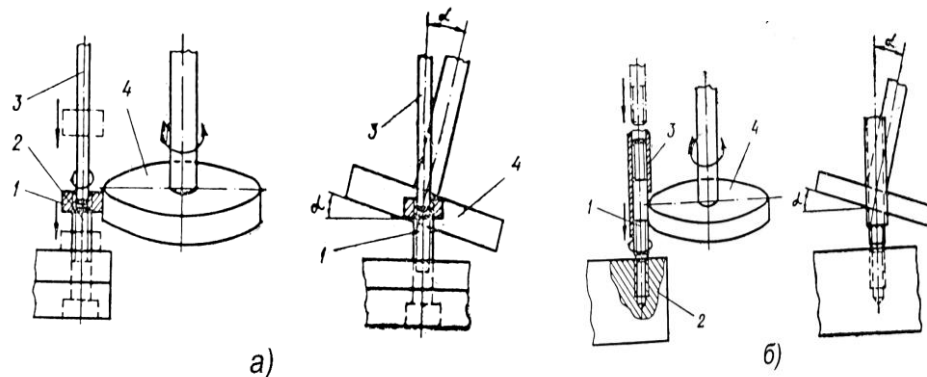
Фрикційно-інерційний спосіб загвинчування: а- гайок: 1- гайка; 2-болт; 3- напрямний стержень; б-шпильок: 1- шпилька; 2- корпус; 3- напрямна втулка.
